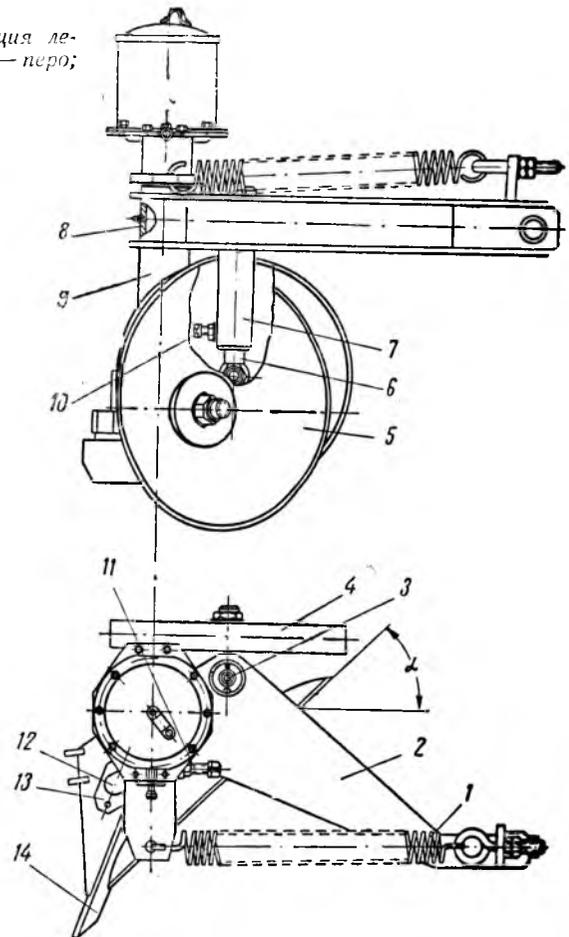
Секция левая: 1 — пружина; 2 — брус тяговый; 3 — винт подъемный; 4 — колесо; 5 — диск сферический; 6 — стойка колеса; 7 — стойка направляющая; 8 — втулка стойки рабочего органа; 9 — стойка рабочего органа; 10 — стопорный винт; 11 — регулировочный винт; 12 — семяпровод; 13 — фланец семяпровода; 14 — перо.
